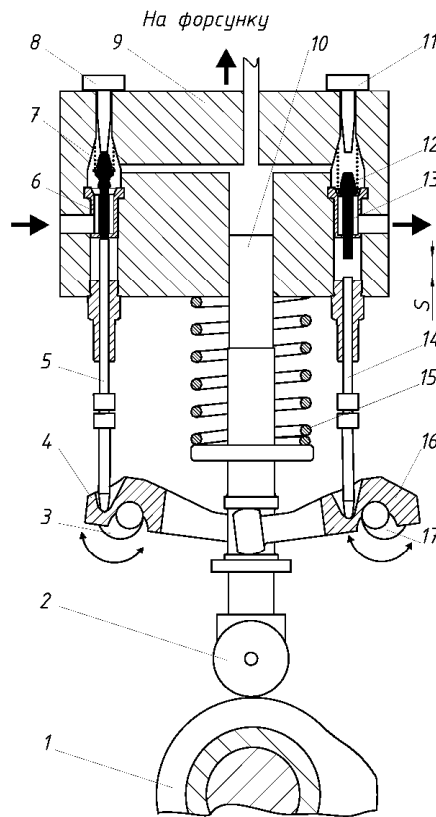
Схема ПНВТ із клапанним регулюванням і механічним приводом клапанів. 1 – кулачковий вал; 2 – ролик штовхача; 3, 17 – ексцентрик; 4 – важіль привода наповнювального клапана; 5, 14 – штанга штовхача; 6 – наповнювальний клапан; 7, 12 – пружина клапана; 8, 11 – обмежник ходу клапана; 9 – корпус; 10 – плунжер; 13 – відсічний клапан; 15 – зворотня пружина плунжера; 16 – важіль привода відсічного клапана
